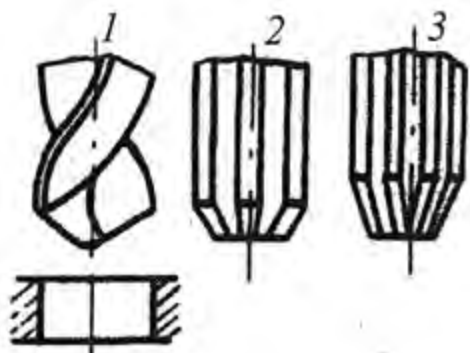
Оброблення отвору трьома інструментами за три переходи
